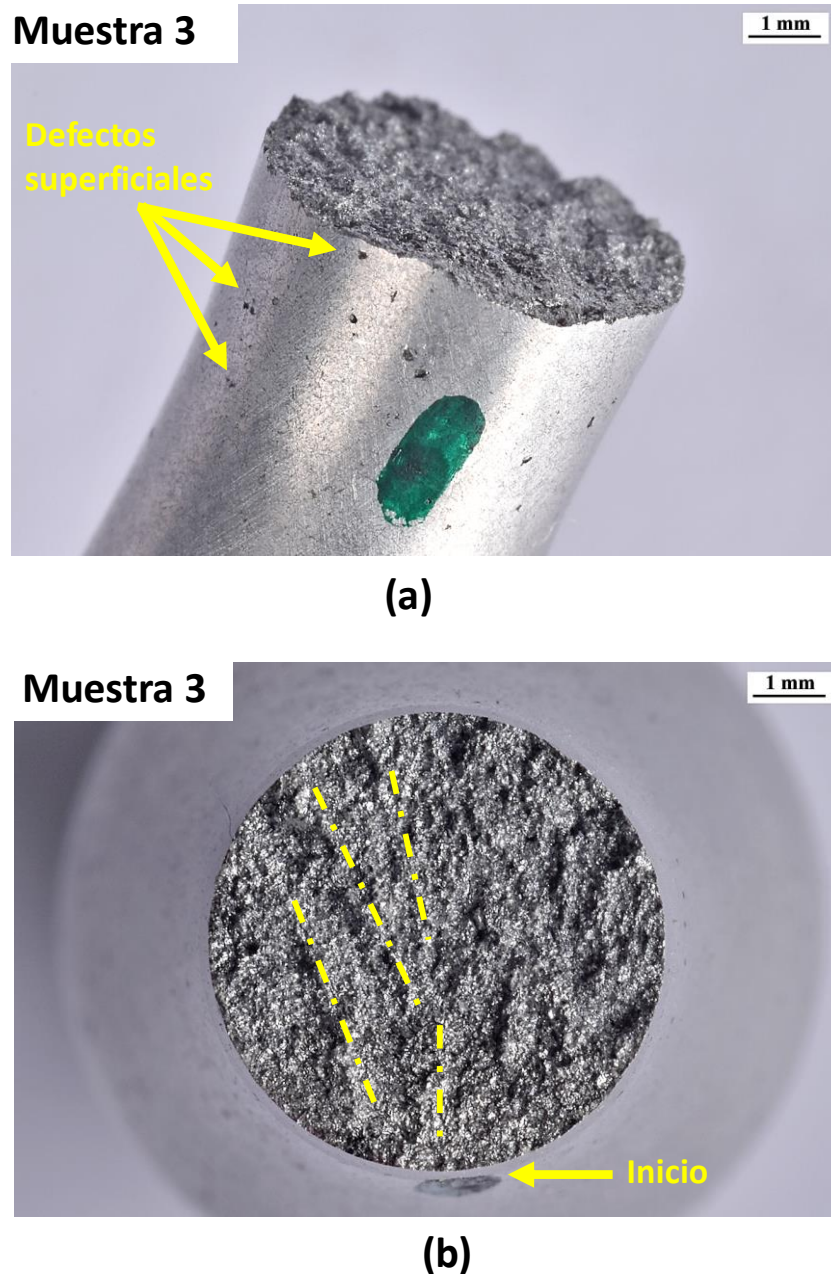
Superficie de fractura de la Muestra 3 (a) vista lateral y (b) vista superior
